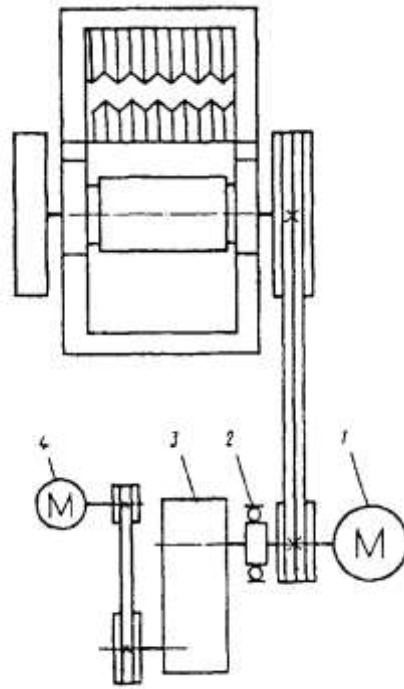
Схема допоміжного привода щоквої дробарки
